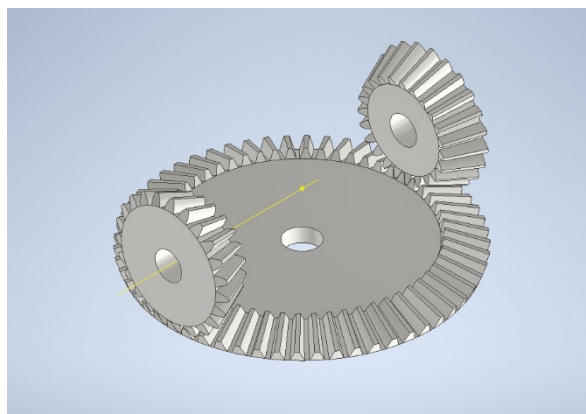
Perspectiva axonométrica del engranaje biselado inferior.
